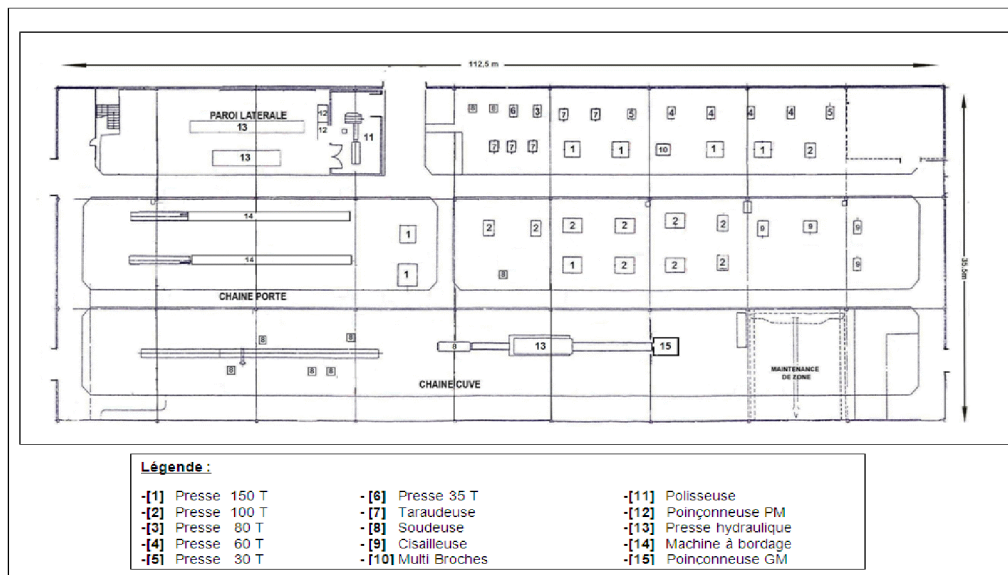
Plan de l'atelier presse et soudure
